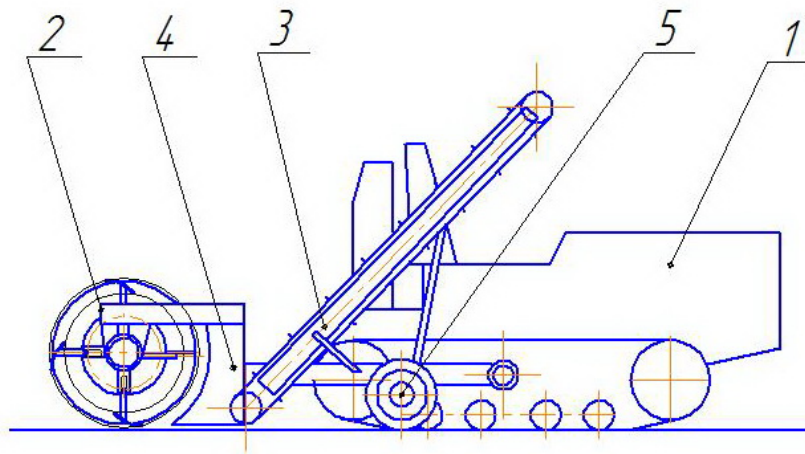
Схема погрузчика-смесителя: 1 – базовый трактор; 2 – шнекофрезерный рабочий орган; 3 – отгрузочный ленточно-планчатый транспортер; 4 – общая рама; 5 – опорное колесо
